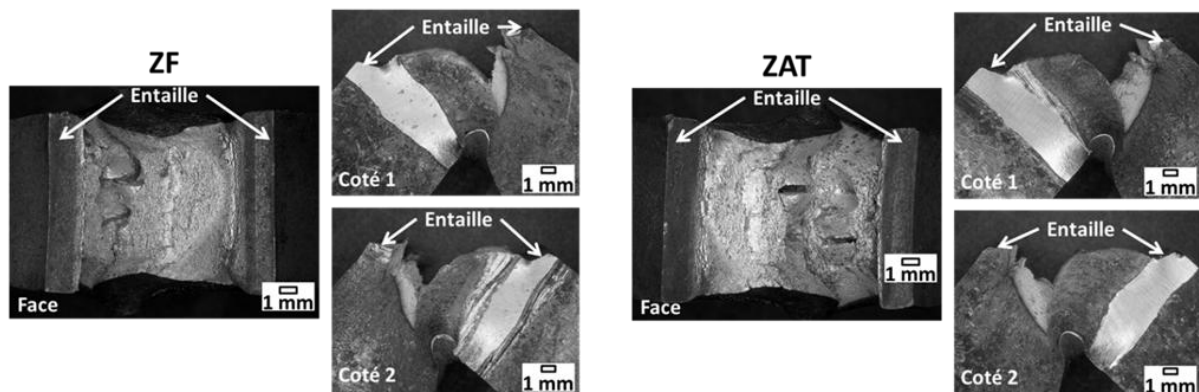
Fractographies des éprouvettes ZF et ZAT après essai Charpy
